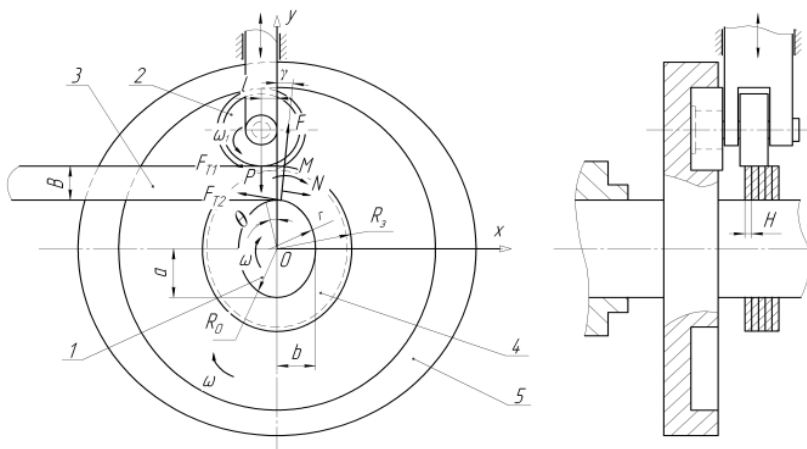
Розрахункова схема процесу навівання гвинтового робочого органу сільхозмашин на оправку: 1 – еліпсна оправка; 2 – притискний ролик; 3 – стрічка; 4 – гвинтовий еліпсний елемент; 5 - торцевий кулачок, форма якого відповідає еквідистанті еліпсної оправки 1
